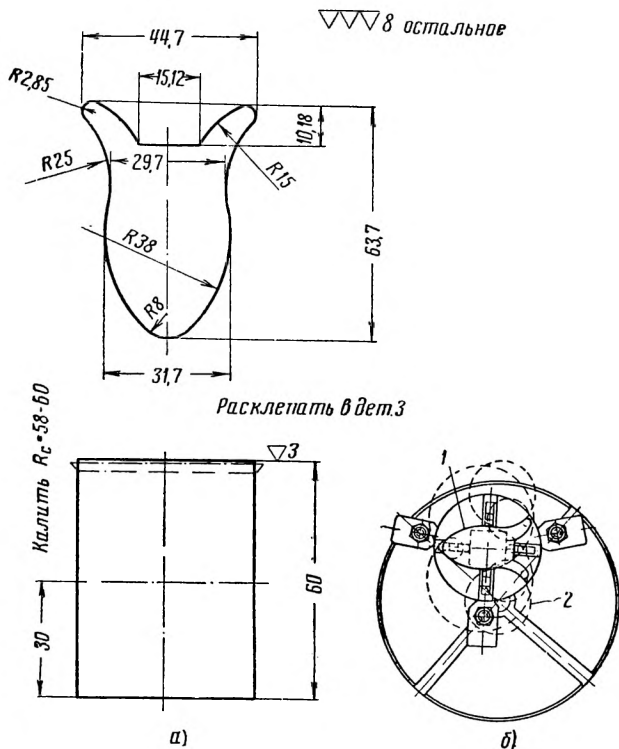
Деталь сложного профиля (а), схема установки и обработки детали на круглом столе (б)
